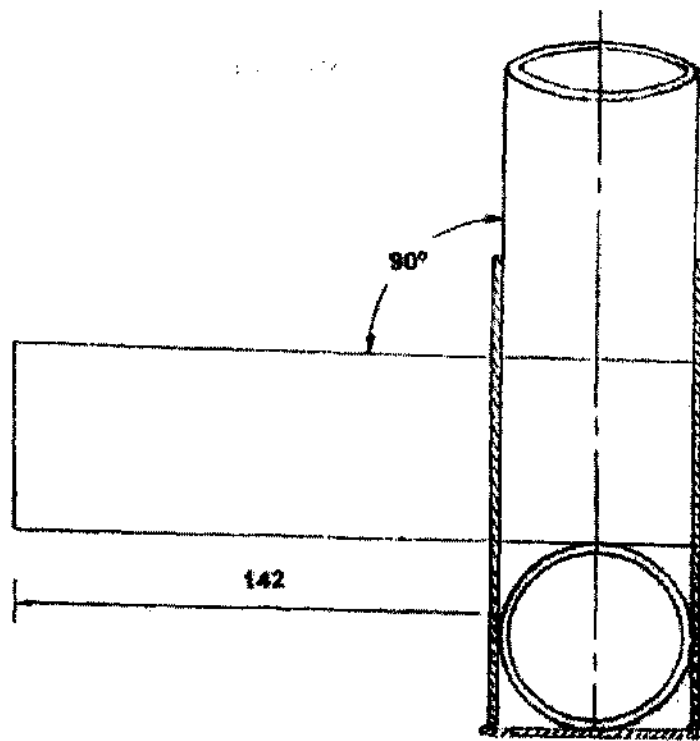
Conexão lateral inferior externa - vista frontal - localização B (medidas em mm)
